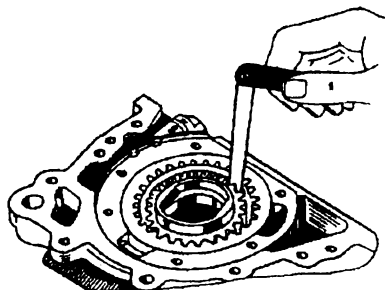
Измерение зазора между наружным диаметром ведущей шестерни и корпусом насоса
